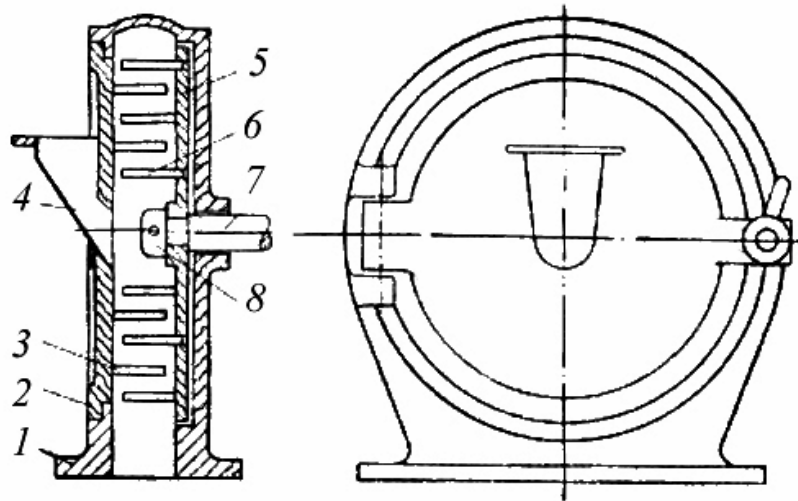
Дисмембратор: 1 – корпус; 2 – відкидна кришка (статор); 3 – біти статора; 4 – приймальна лійка; 5 – диск ротора; 6 – біти ротора; 7 – приводний вал; 8 – затискна гайка
